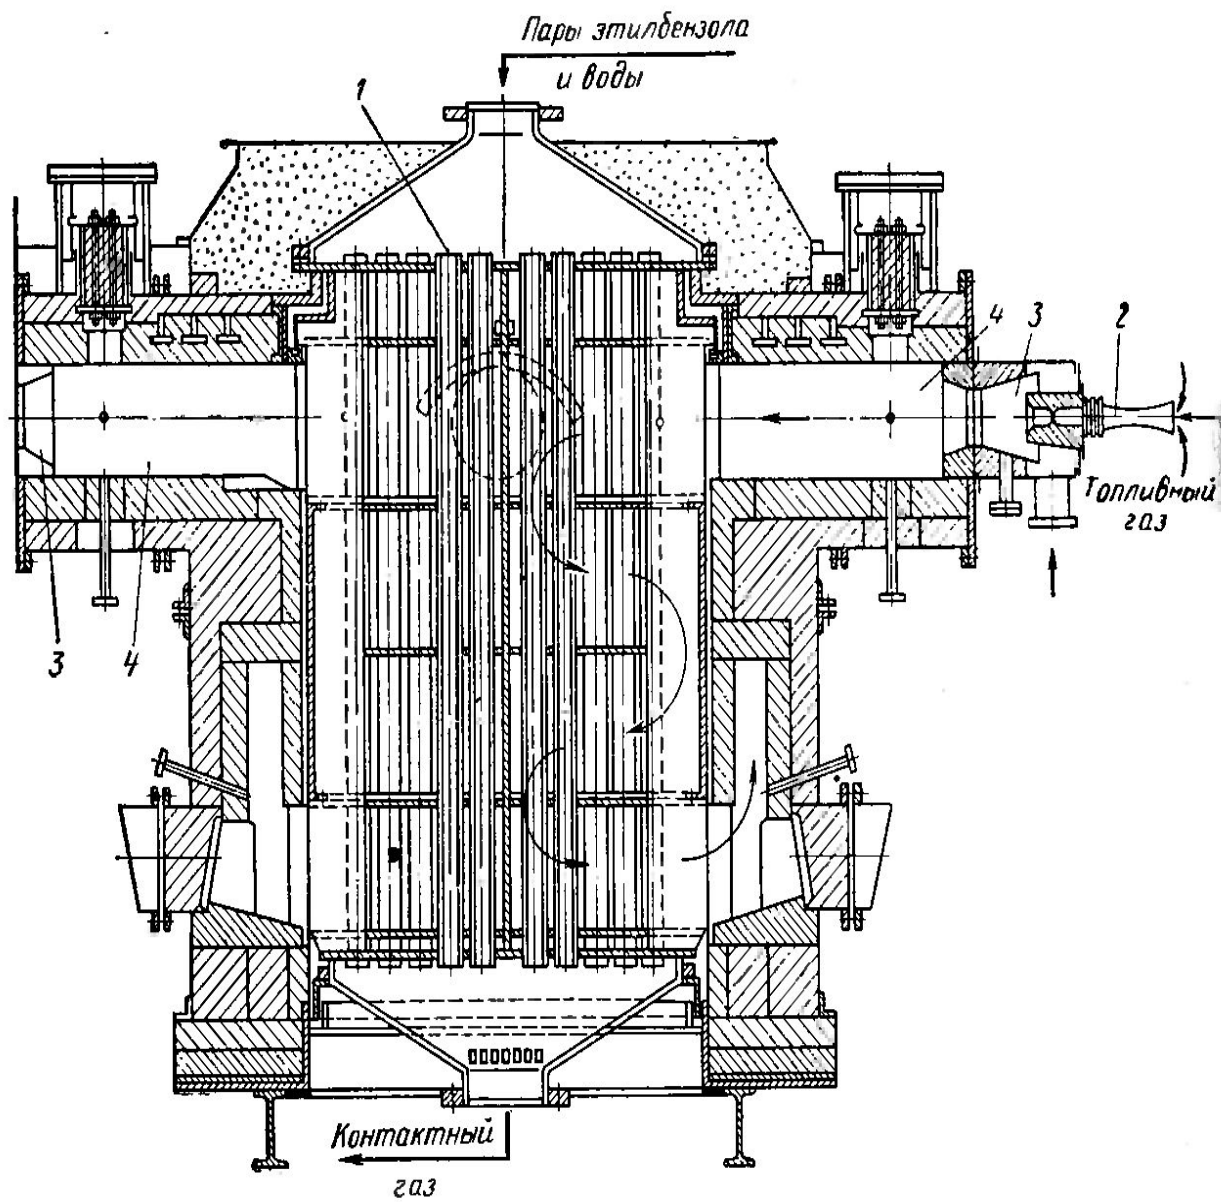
Трубчатый реактор с обогревом дымовыми газами
